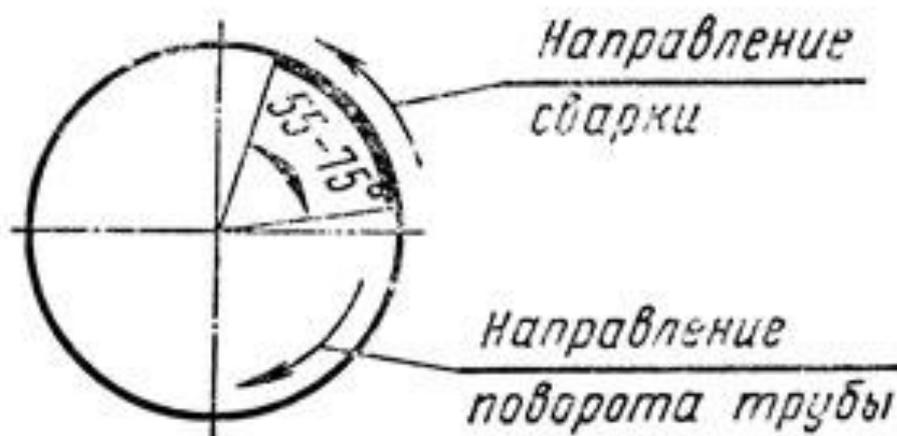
Схема сварки стыка труб малого диаметра
